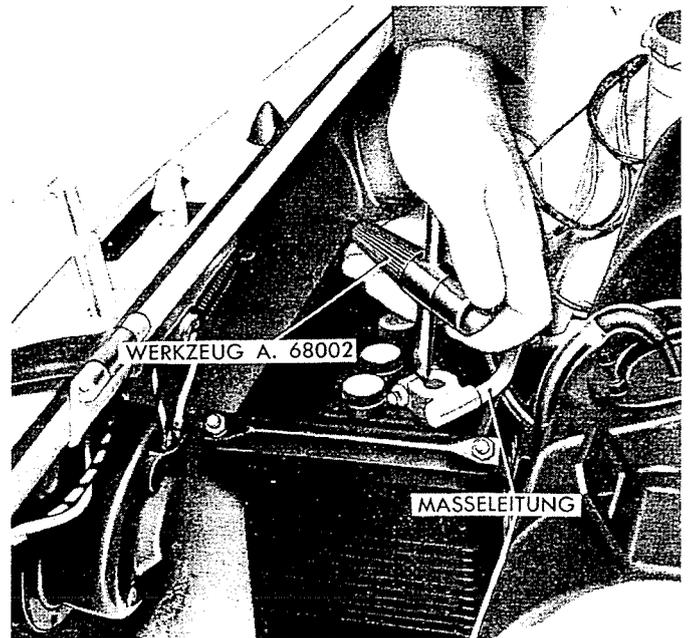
Lösen der Batterieklemmen mit dem Werkzeug A. 68002.
